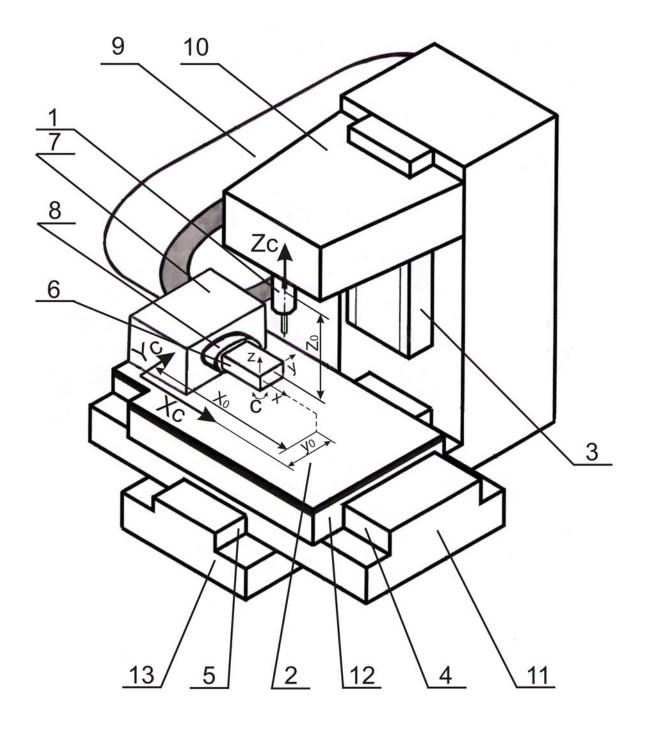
Структурная схема вертикального ОЦ: I — шпиндель; 2 — рабочий стол; 3,4,5 — направляющие; 6 — обрабатываемая деталь; 7 — поворотная головка; 8 — патрон; 9 — инструментальный магазин; 10,11,12 — подвижные элементы; 13 — основание; C — обозначение поворота детали; $X_{\rm c}$, $Y_{\rm c}$, $Z_{\rm c}$ — координатные оси системы координат станка; X, Y, Z — координатные оси системы координат детали; X_0 , Y_0 , Z_0 — константы смещения нулевой точки системы координат детали
